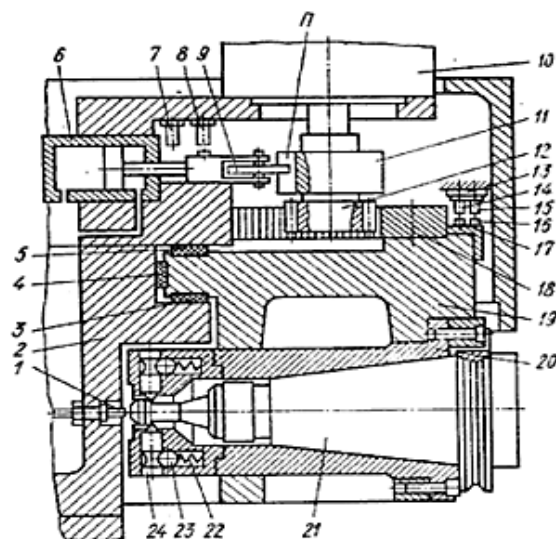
Привод повороту й фіксація інструментального магазину
